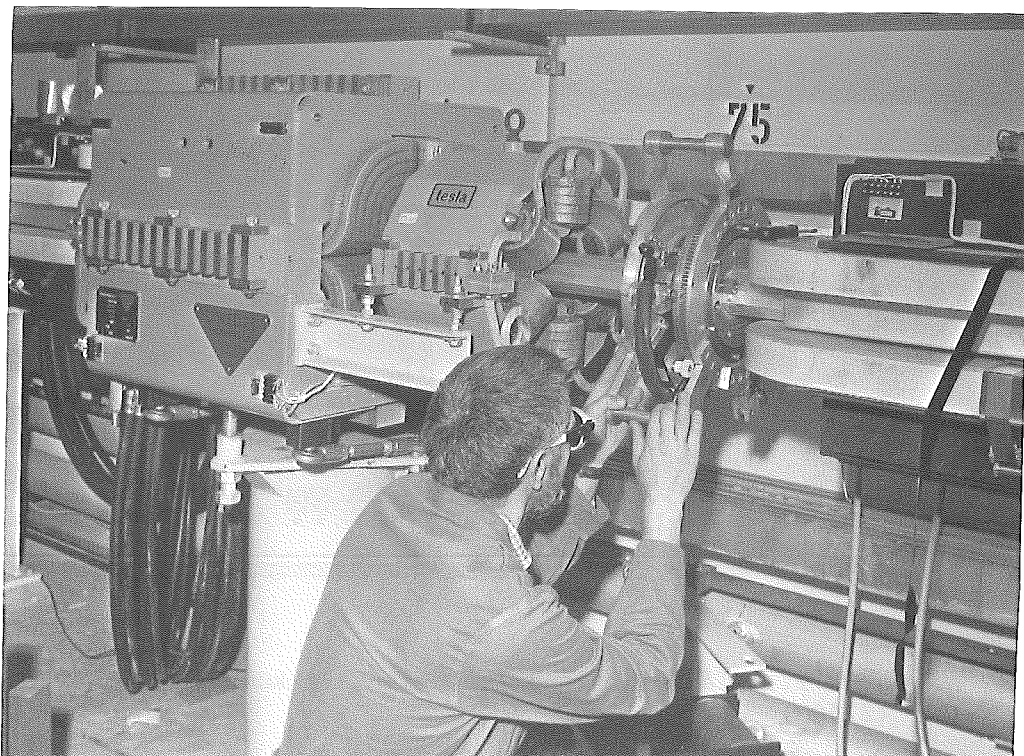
Maschine zum Schweißen der Vakuumbälge
